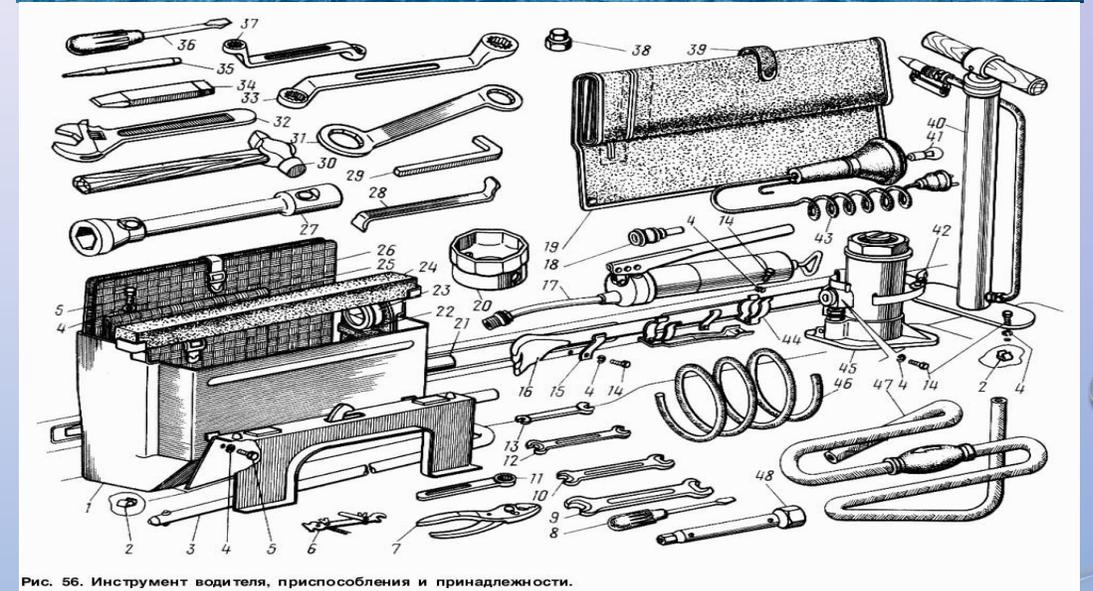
Инструмент водителя, приспособления и принадлежности.
